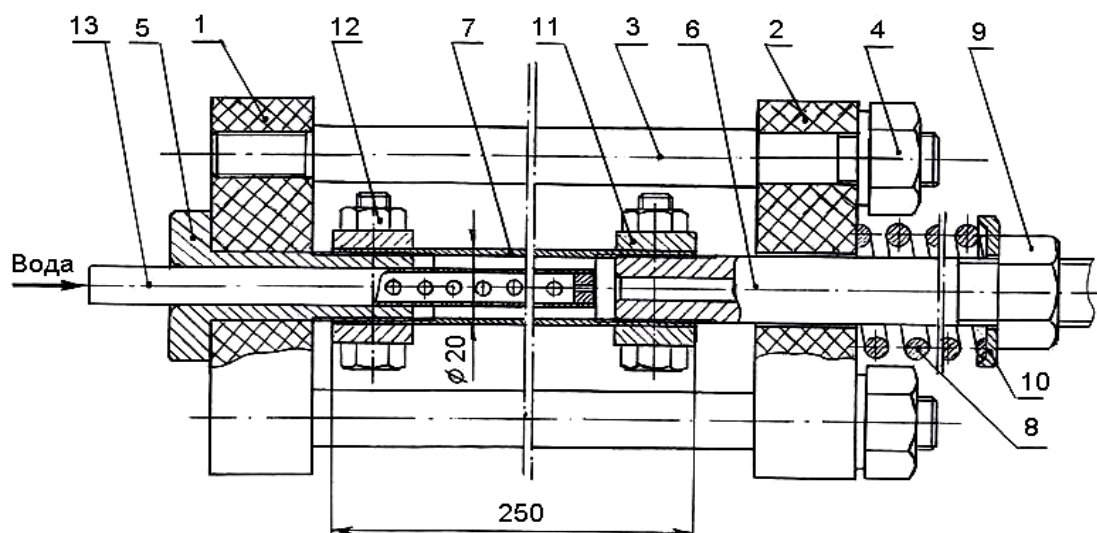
Конструктивная схема лабораторной установки: 1,2 – поперечины; 3 – стяжные шпильки; 4 – гайка; 5 – неподвижный захват; 6 – подвижный захват; 7 – образец трубы; 8 – пружина; 9 – гайка; 10 – шайба; 11 – контакт; 12 – стяжной болт; 13 – перфорированная трубка
